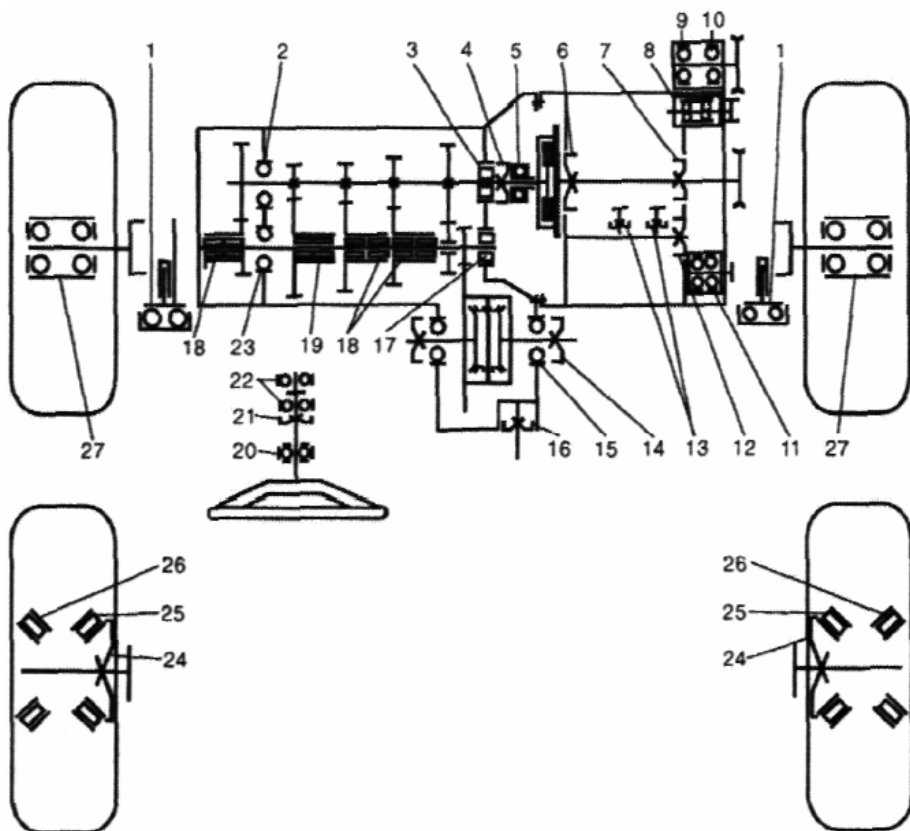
Схема расположения подшипников качения и манжетных уплотнителей (см. позиции в таблицах приложений 4 и 5).
